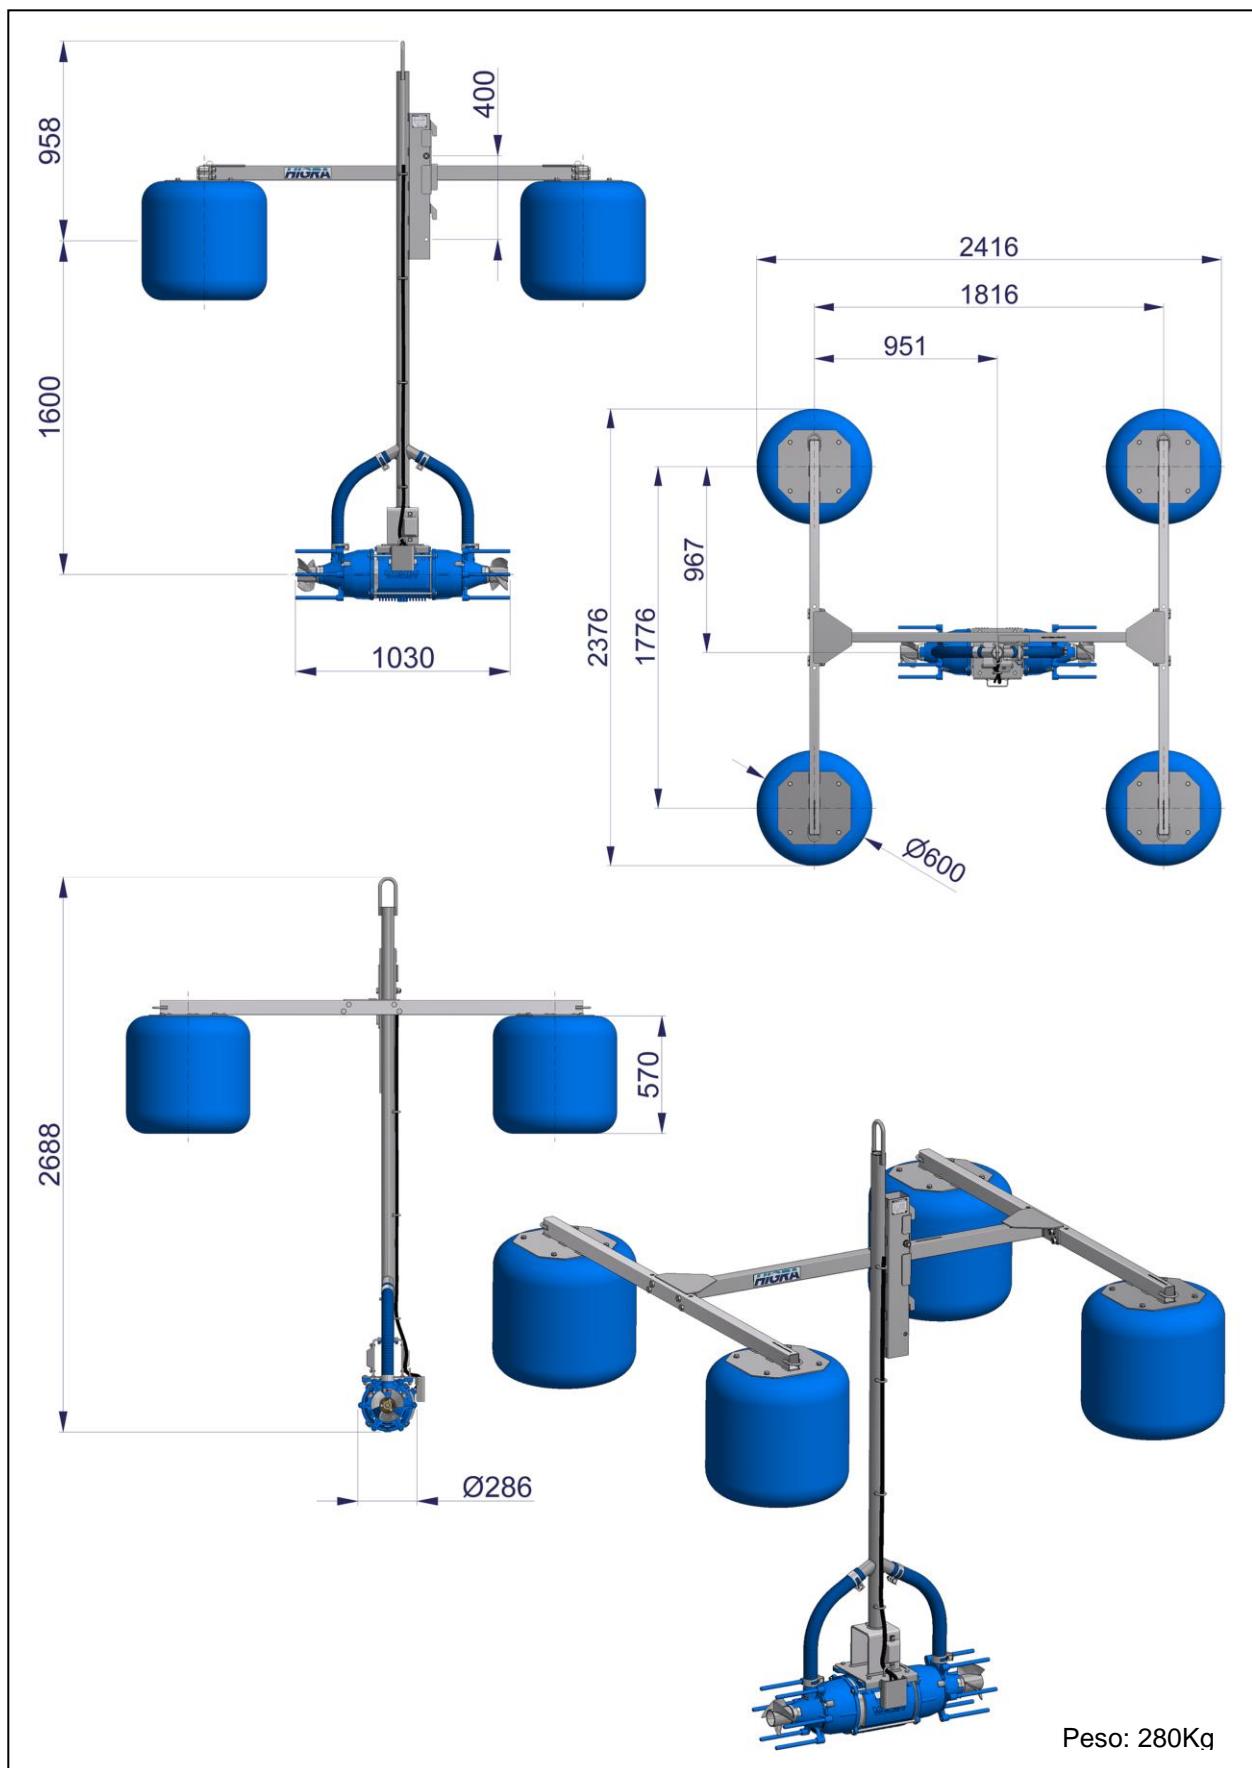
Dimensional TORNADO BITURBO 10, 12,5,15 e 20CV
